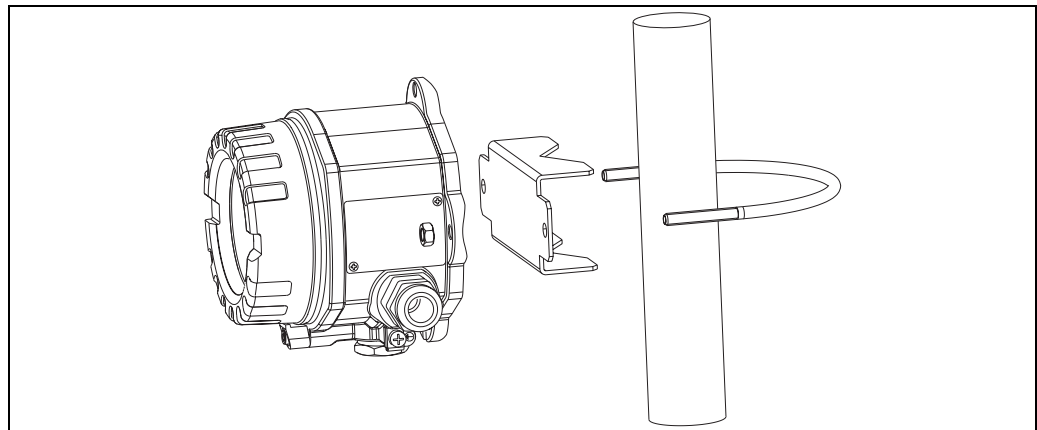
Montage des Feldtransmitters mit Montagehalter, siehe Kap. 'Zubehör'
